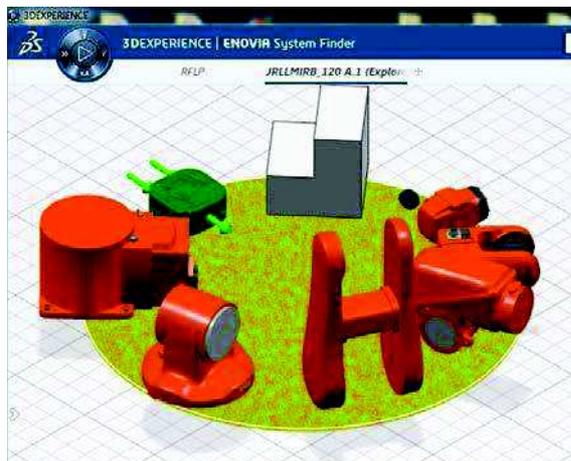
Diseño geométrico de los componentes mecánicos mediante CATIA® Part Design, y presentación en ENOVIA® system finder.
